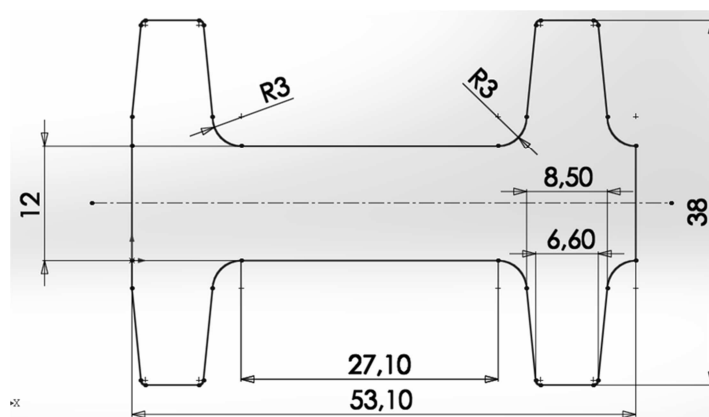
Розгортка поковки з розмірами (вигляд зверху)
